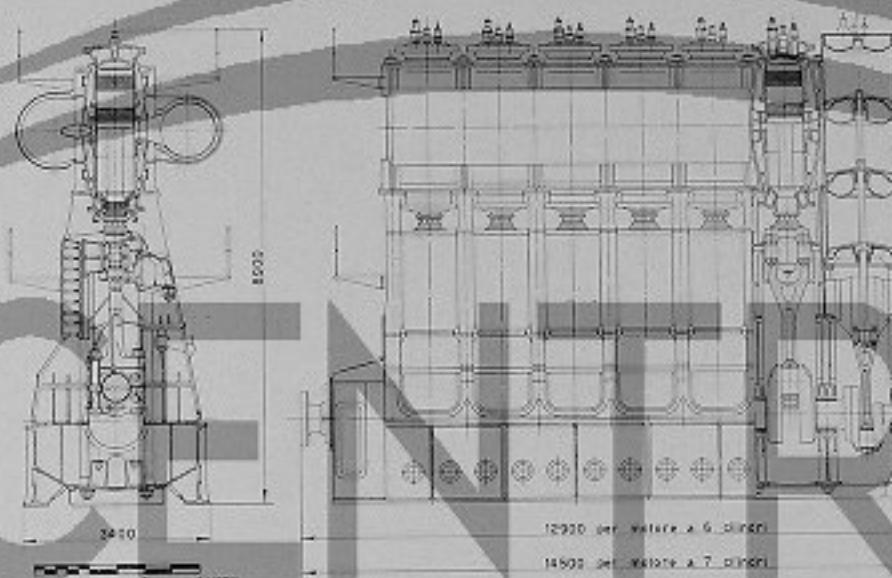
Sezione trasversale e longitudinale del motore a doppio effetto con cilindri di Ø 600 mm
